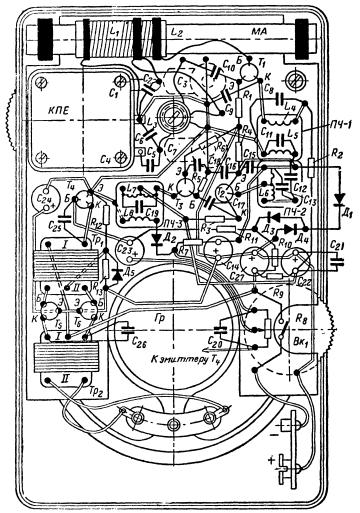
Внешний вид монтажа деталей карманного приемника.
